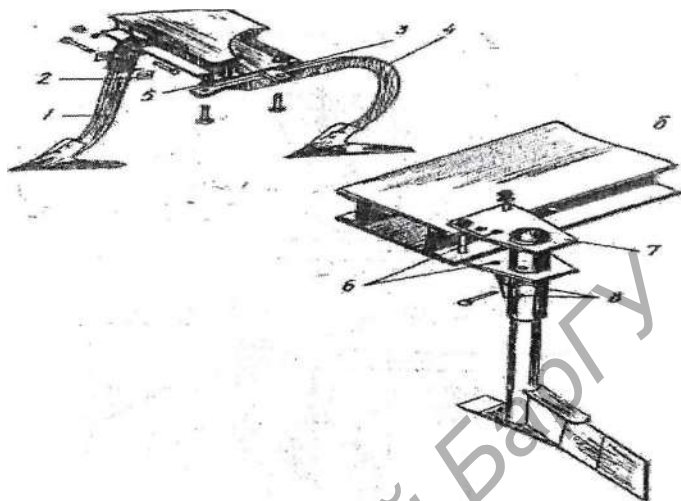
Регулировка положения стоек лап и угла поворота крыла вертикального ножа:
